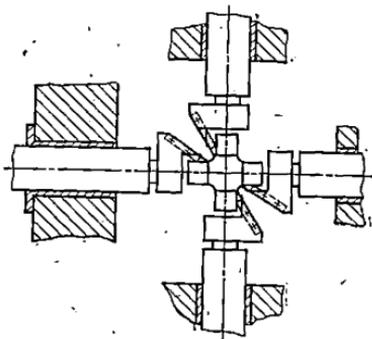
Наладка агрегатного станка для обтачивания цапф крестовины.
